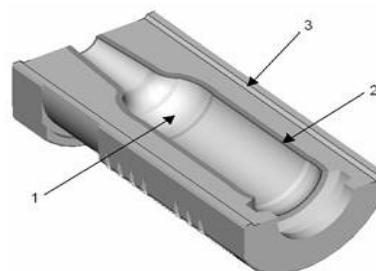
Чистовая полуформа (0,5 л): 1 – формирующая поверхность; 2 – кромка рабочая; 3 – замок сцепления
